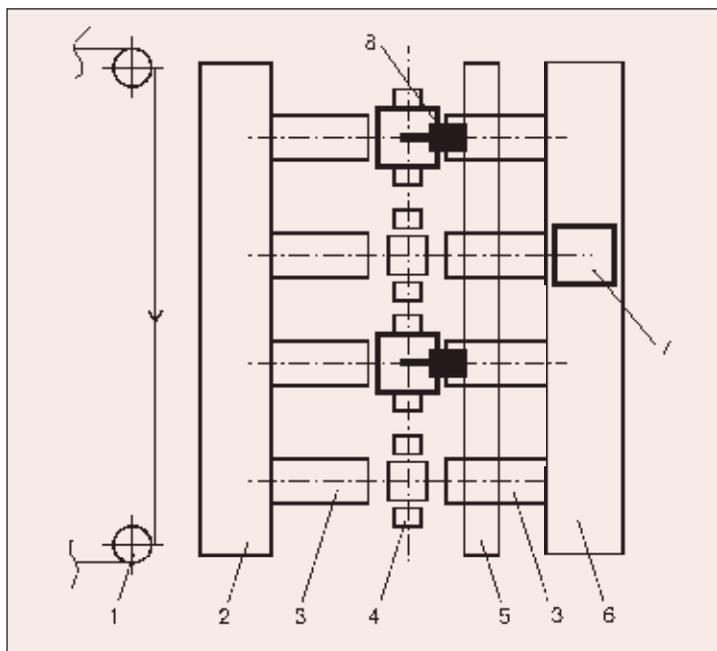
Алгоритм изготовления сварных конструкций в ГПС
